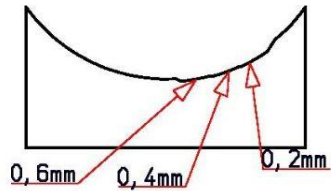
Les profondeurs de coupe sur la jauge à coupeaux
